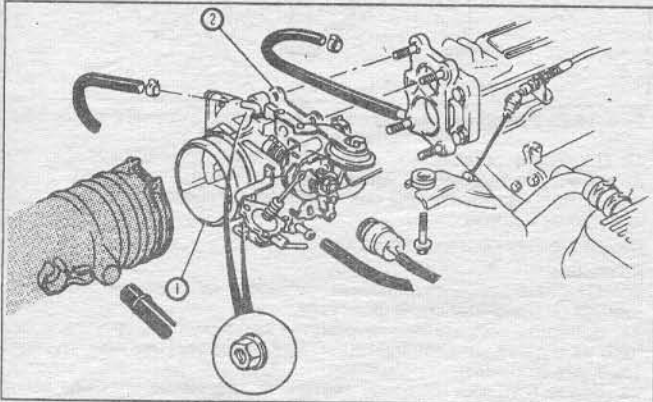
Сборка корпуса дроссельной заслонки: 1 - корпус; 2 - прокладка.
